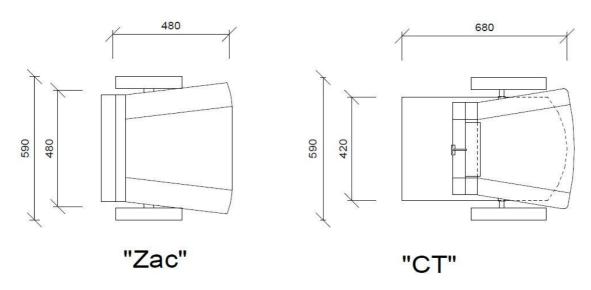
Grundrisse: ZAC und CT
